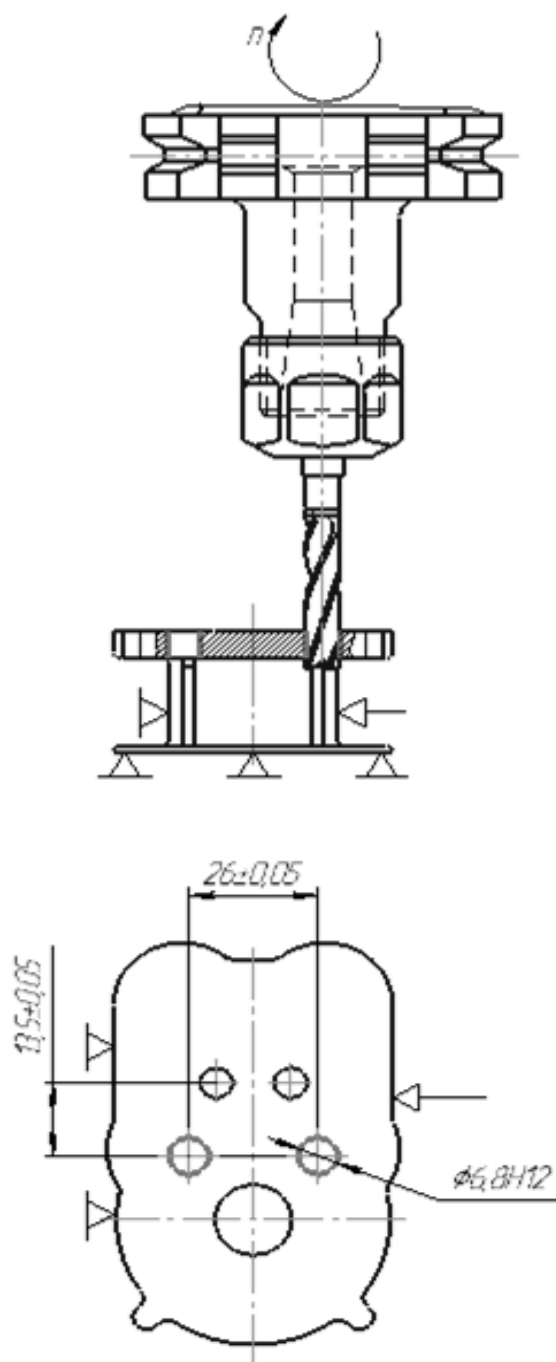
Эскиз обрабатываемой поверхности
